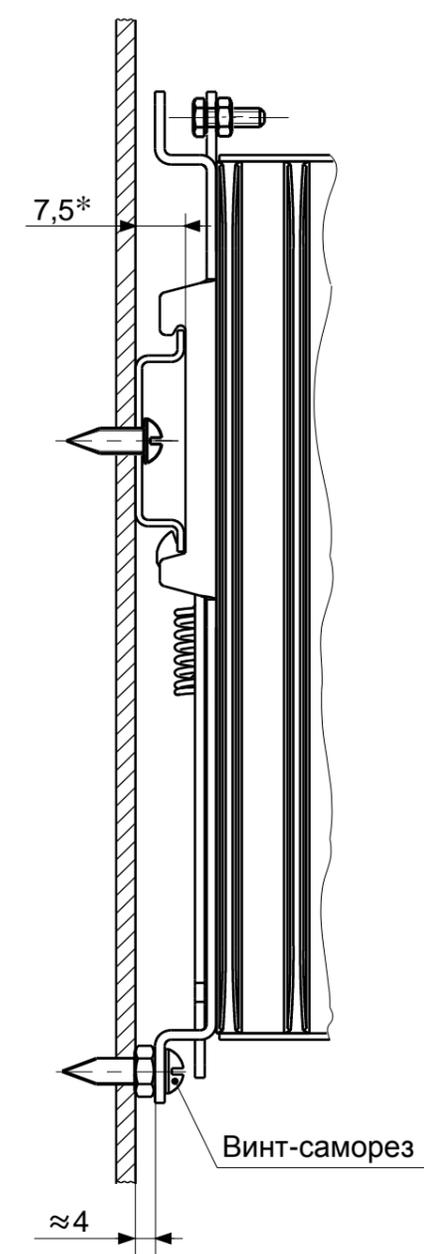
Габаритные и присоединительные размеры ФУ-3
